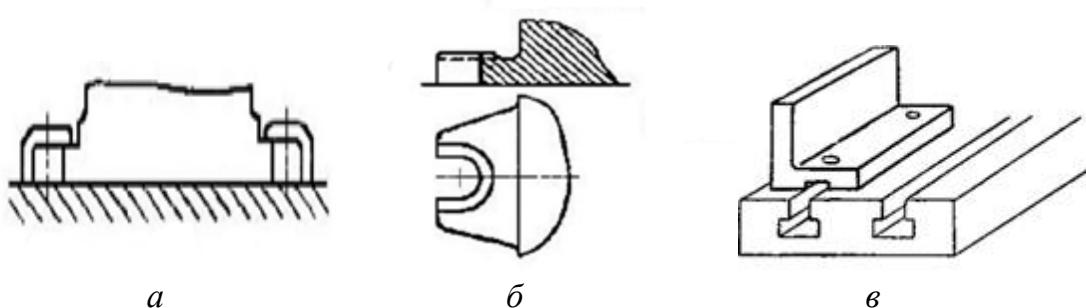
Конструктивные элементы корпусов для крепления приспособлений на столах станков:
